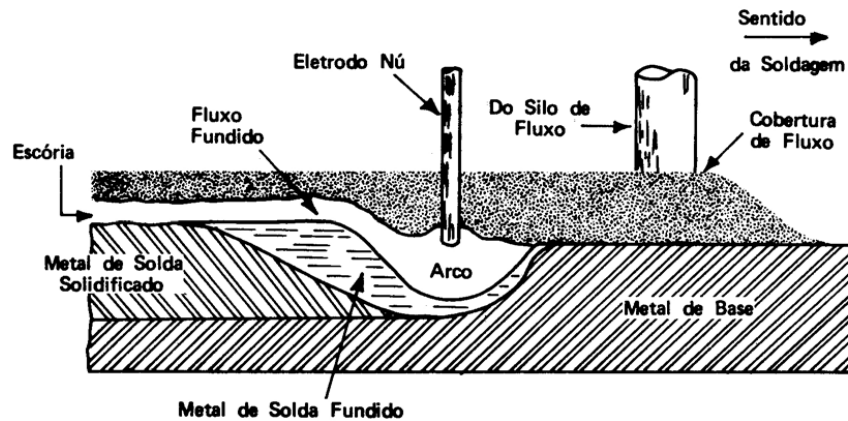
Esquema de soldadura com arco submerso [16]
